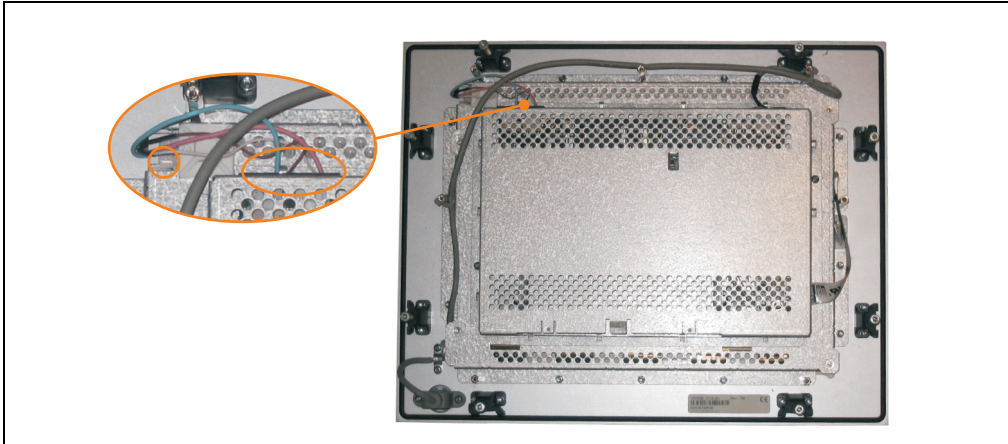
Automation Panel 12,1“ - Schrauben und Stecker lösen
